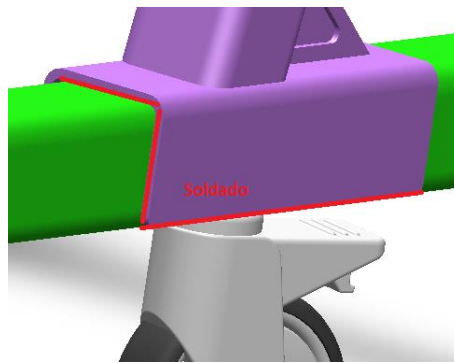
Vista de soldado de pieza N°3 con pieza N°1 (Fuente 89)
